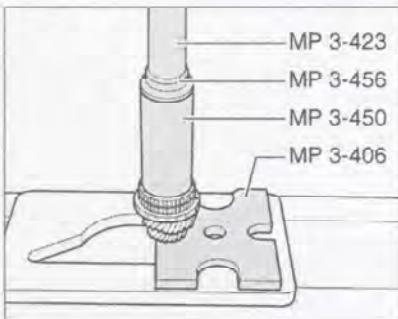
Установка ступицы и скользящей муфты синхронизатора 3-й/4-й передач.
